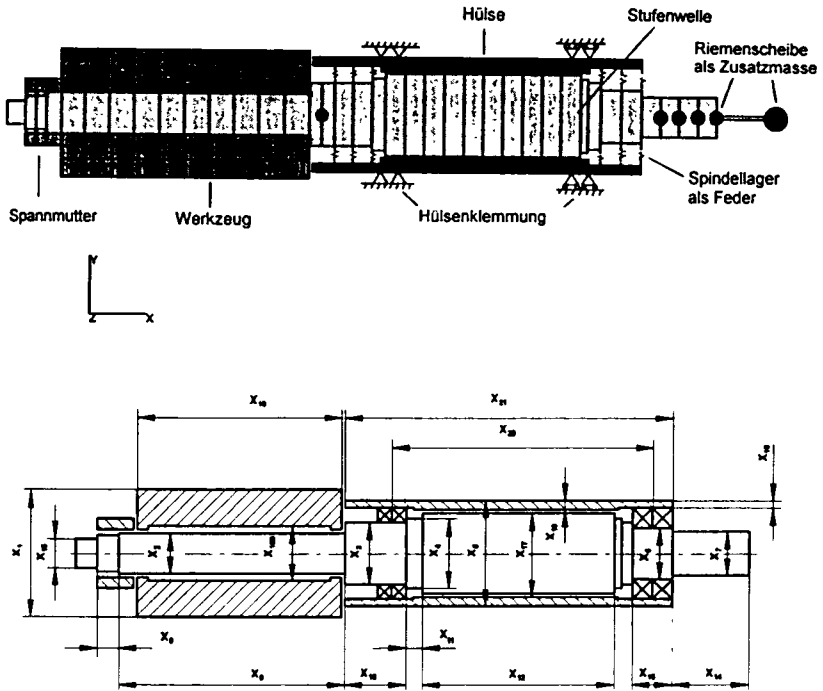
FE-Modell einer berechneten Spindelbaugruppe einer Kehlmaschine und das dazugehörige Parametermodell
